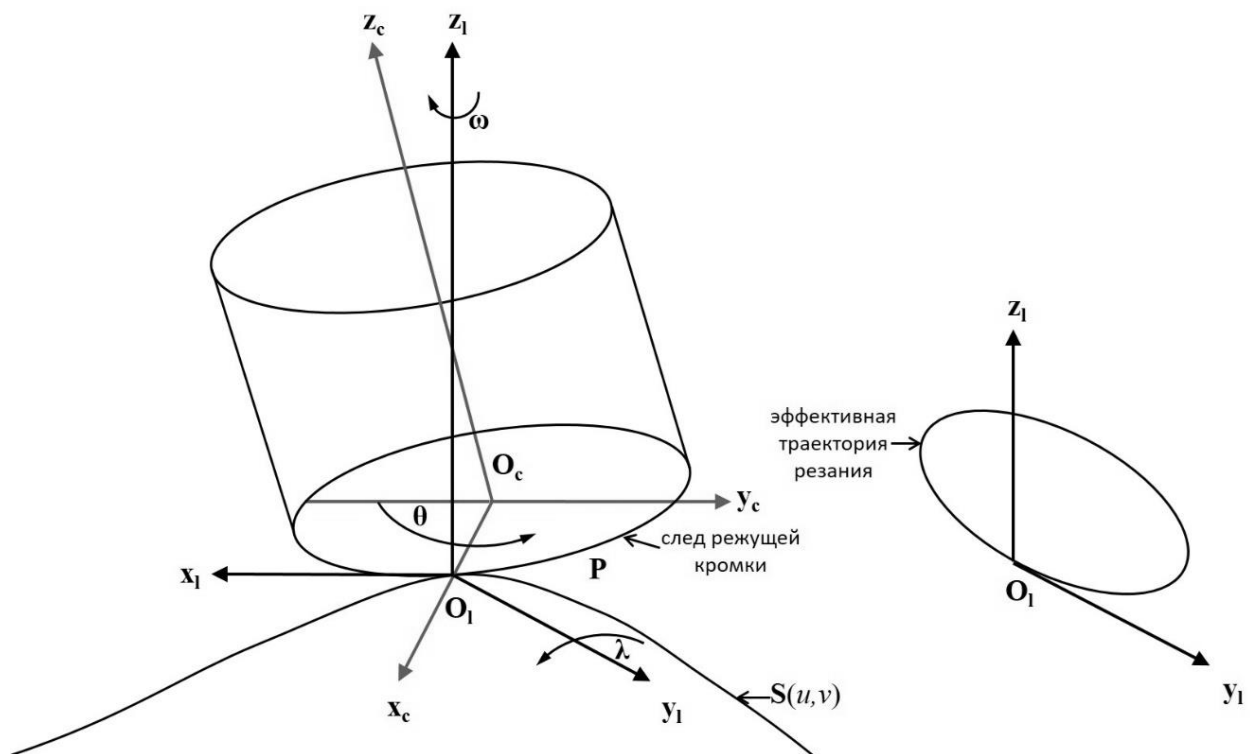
Кинематическая схема процесса пятикоординатного фрезерования
